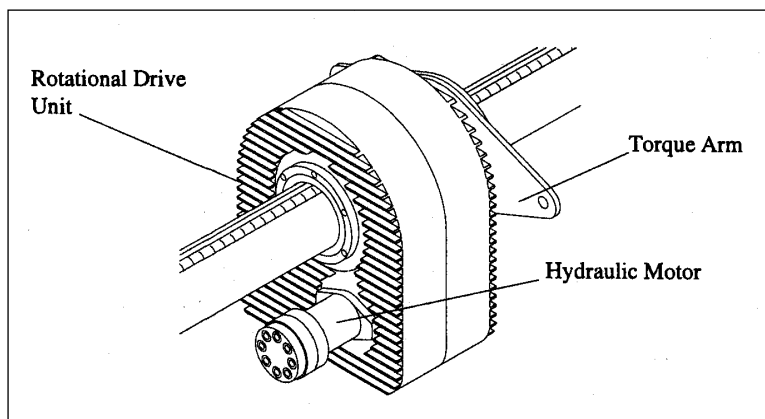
Установка гидравлического двигателя и упоров на узел поворотного привода
